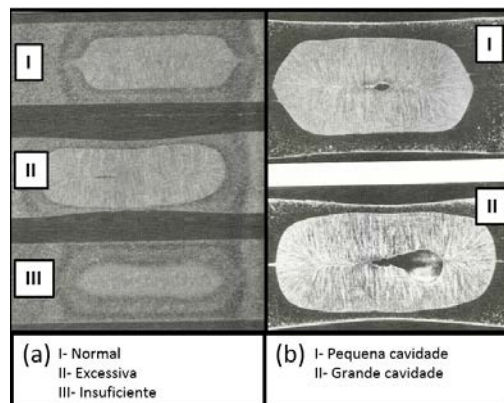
(a) Penetração no ponto de solda; (b) Cavidades no ponto de solda.
